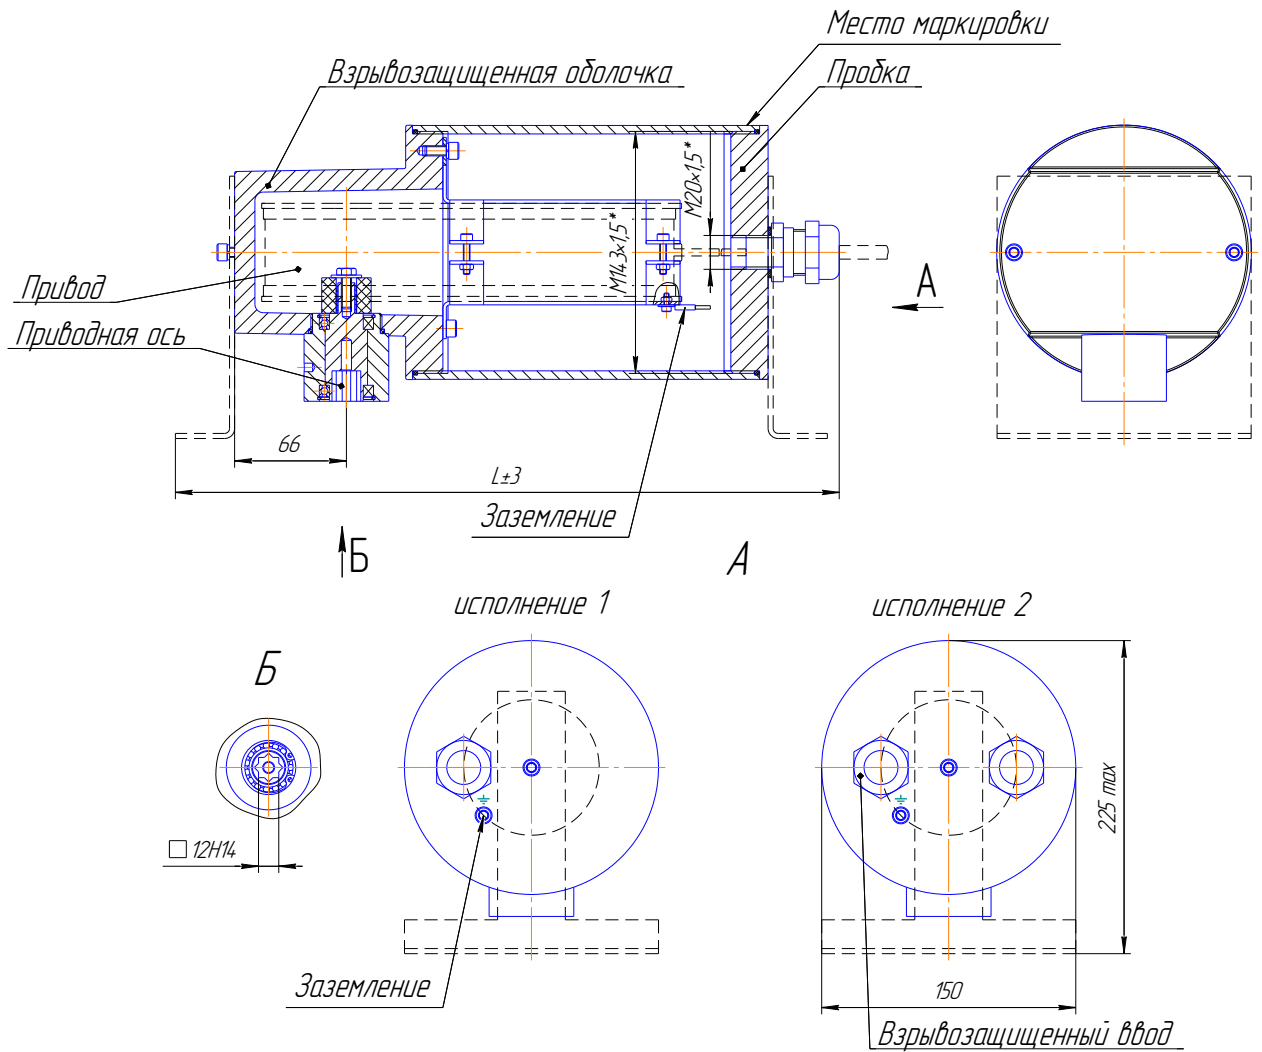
Габаритный чертёж электропривода ЭПВ
